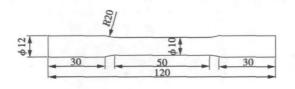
拉伸试样(mm) Fig. 1 Tensile test specimen
